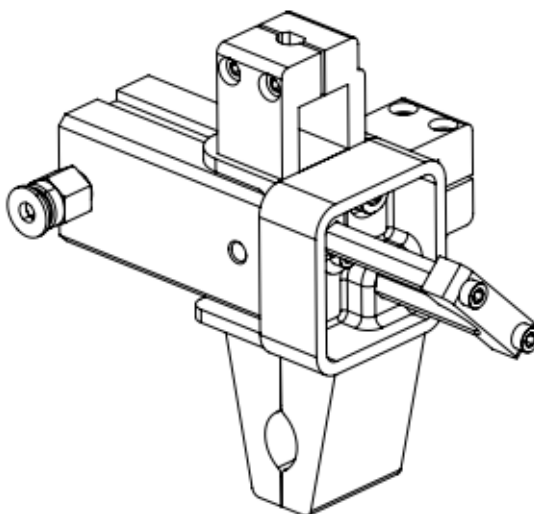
Сменный захват механический с пневматическим приводом
